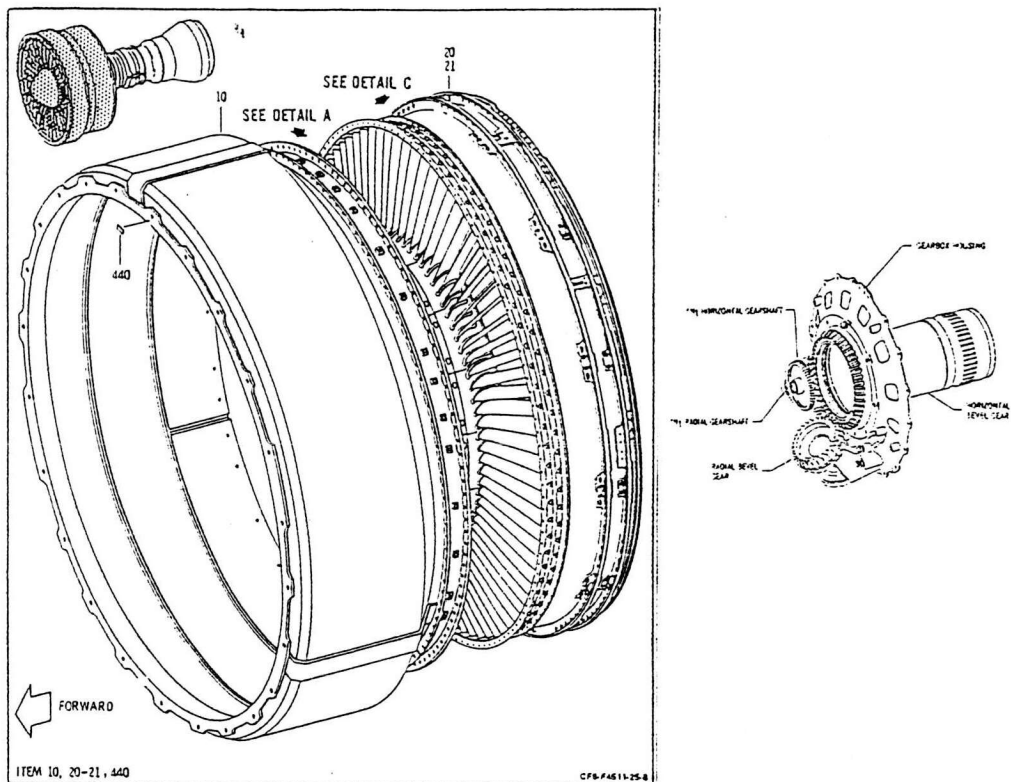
แสดงภาพ 4F Module (Turbine Rear Frame Assembly)
